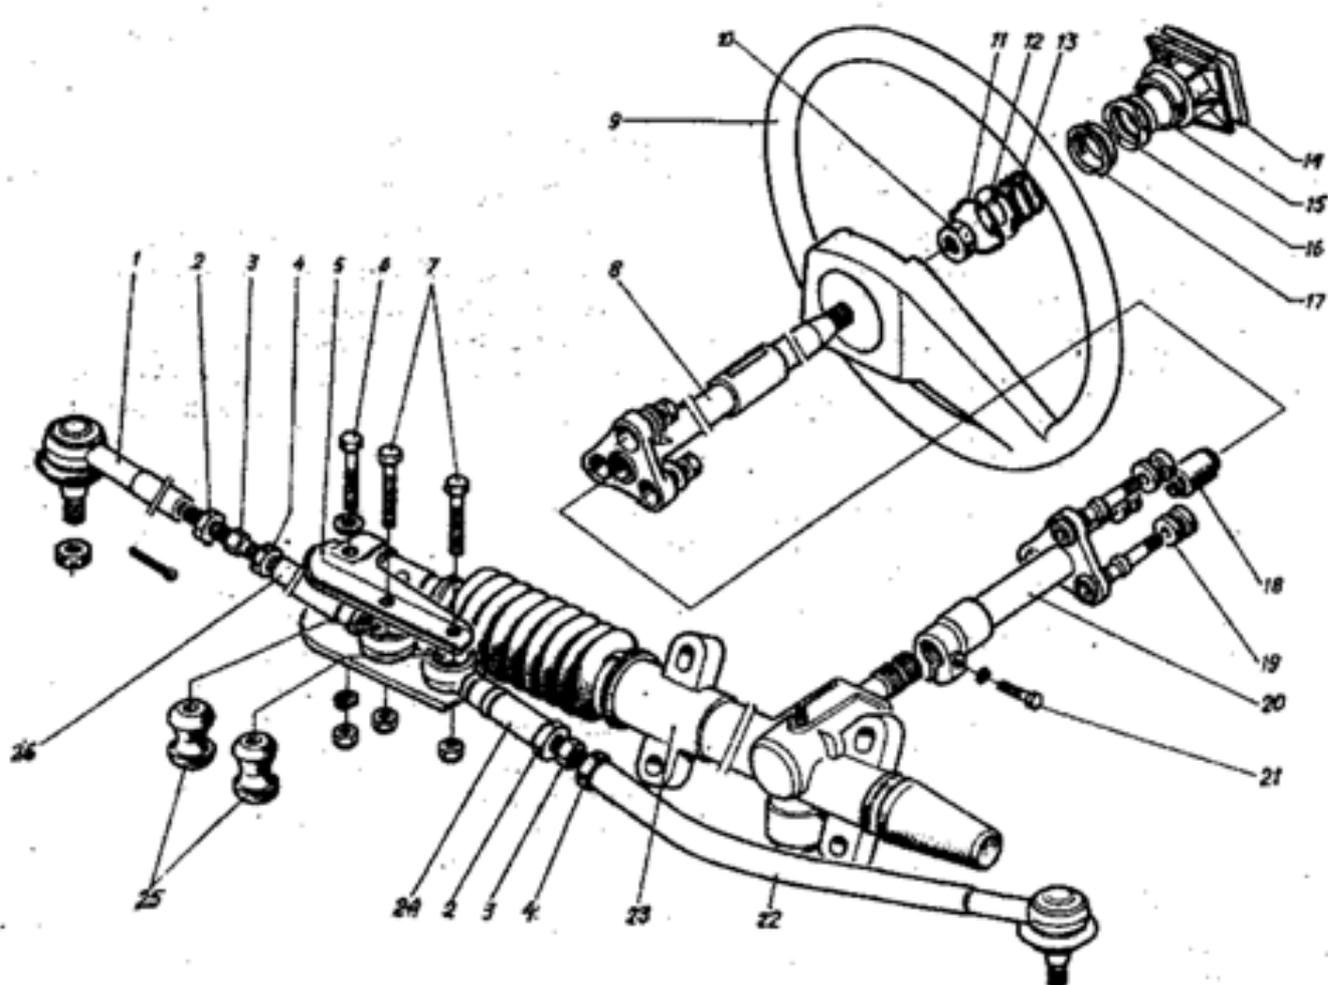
Детали рулевого управления: 1 - половина правой тяги наружная; 2 - контргайка правая; 3 - стяжка тяг; 4 - контргайка левая; 5 - кронштейн тяг; 6 - болт крепления кронштейна; 7 - болт крепления шарнира; 8 - вал верхний; 9 - колесо рулевое; 10 - гайка рулевого колеса; 11 - кольцо стопорное; 12 - крышка опорная; 13 - пружина; 14 - крышка включателя сигнала; 15 - оправа; 16 - включатель сигнала; 17 - кольцо контактное верхнее; 18 - буфер; 19 - втулка муфты; 20 - вал нижний; 21 - болт клеммного соединения; 22 - половина левой тяги наружная; 23 - механизм рулевой в сборе; 24 - половина левой тяги внутренняя; 25 - шарнир внутренний; 26 - половина правой тяги внутренняя.
